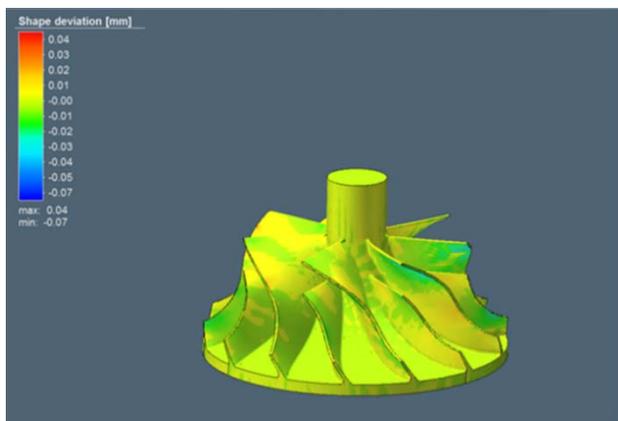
Суммарные деформации масштабированной заготовки крыльчатки компрессора
